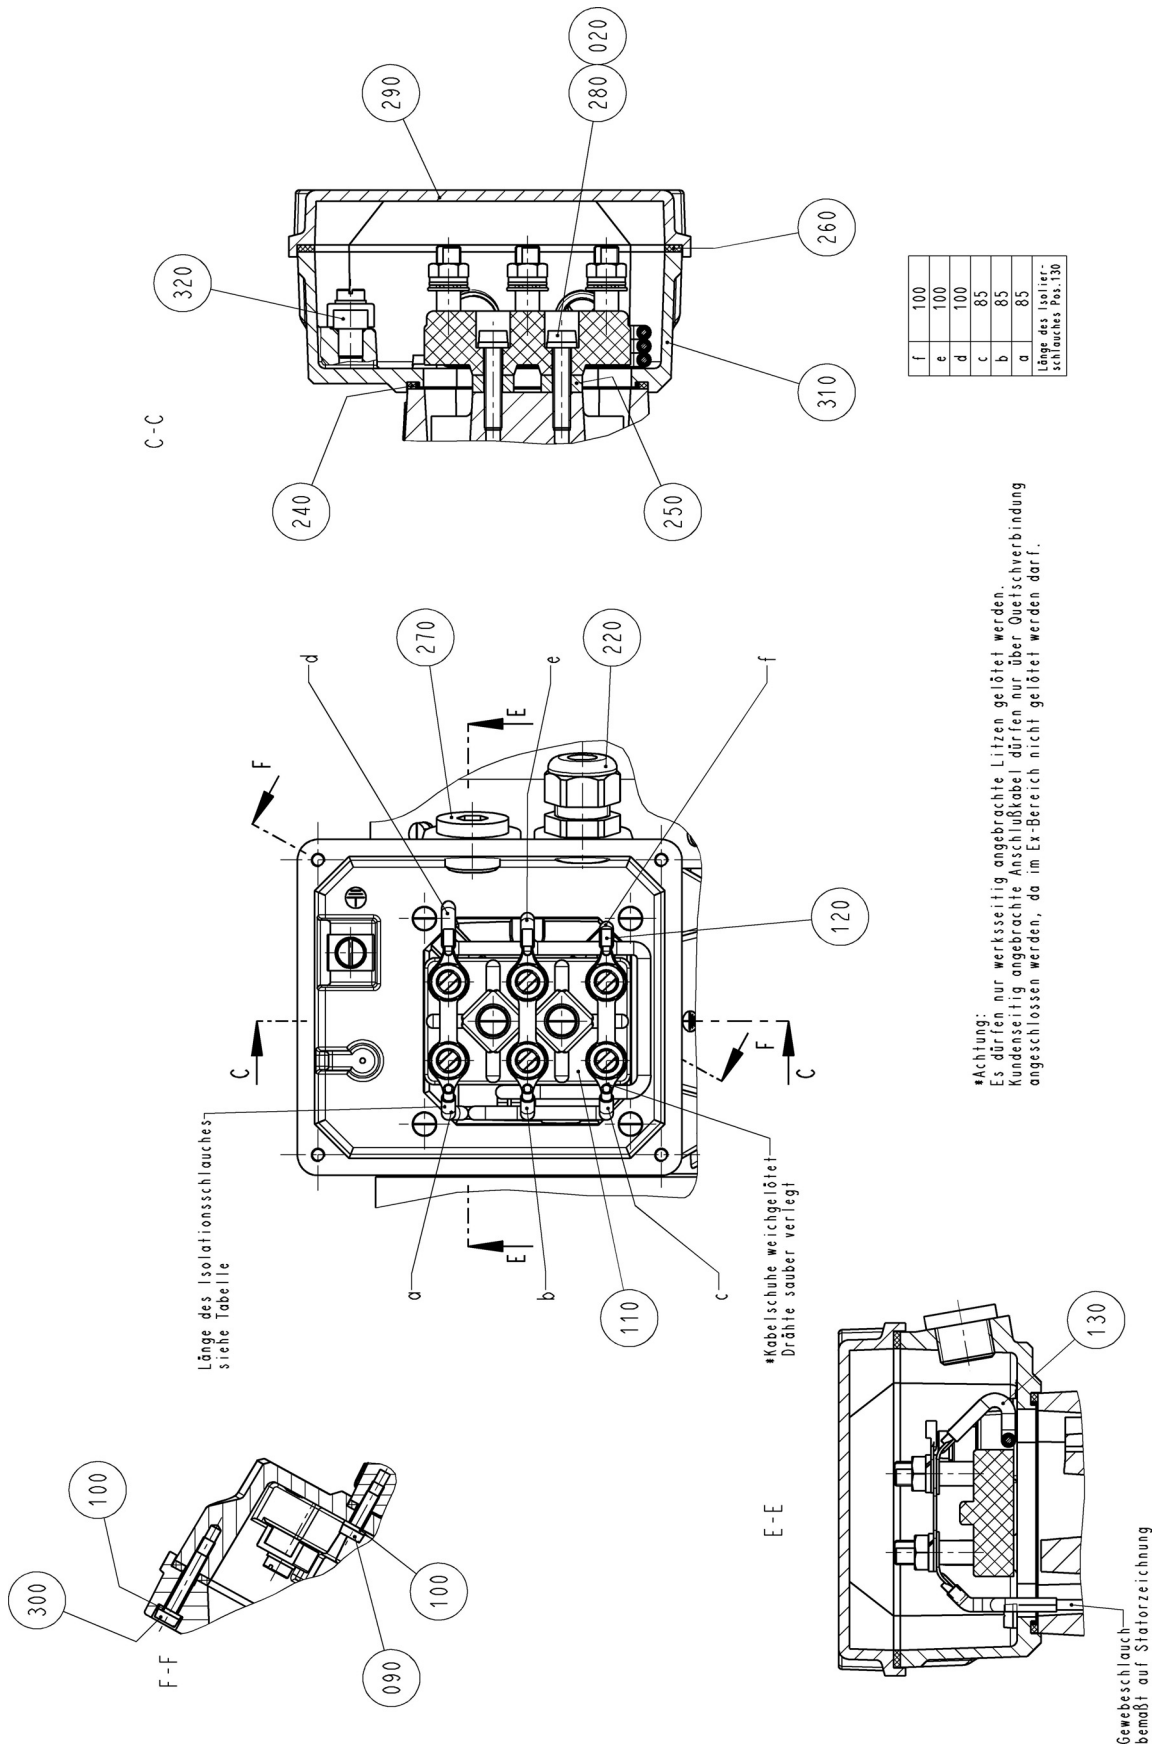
Klemmkasten Explosionsgeschützter Drehstrommotor
